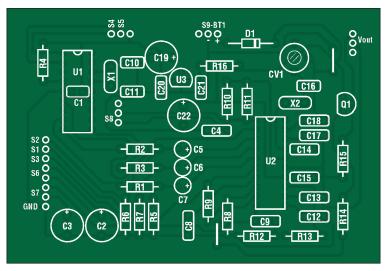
PCB lato componenti del generatore video in scala1:1.
